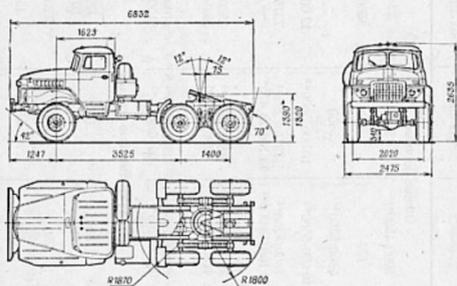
Габаритный чертеж седельного тягача Урал-375СН
